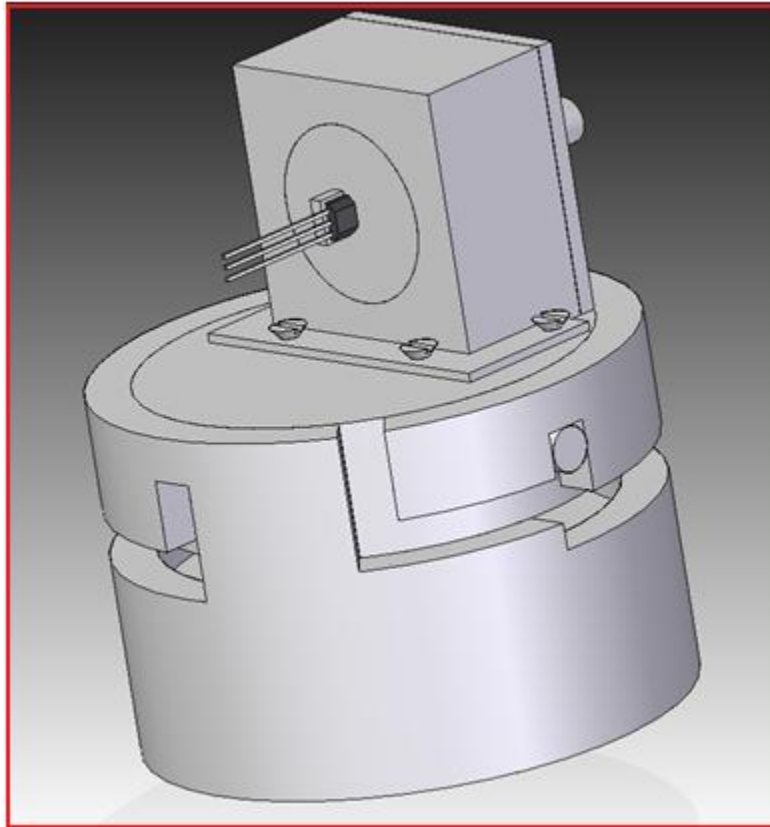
Diseño definitivo en Solid Edge de magnetómetro de muelles, posición 2
